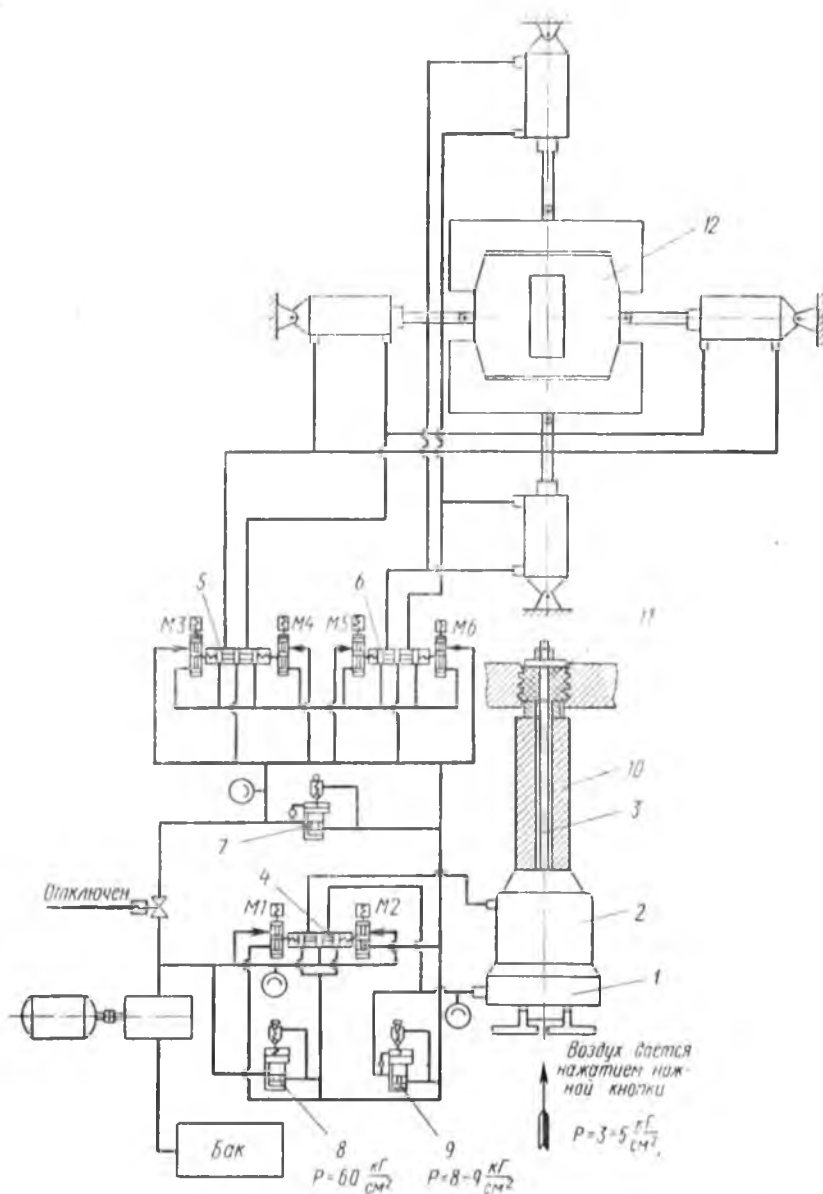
Схема станка для формовки гофр резиновым пуансоном по жесткой матрице
